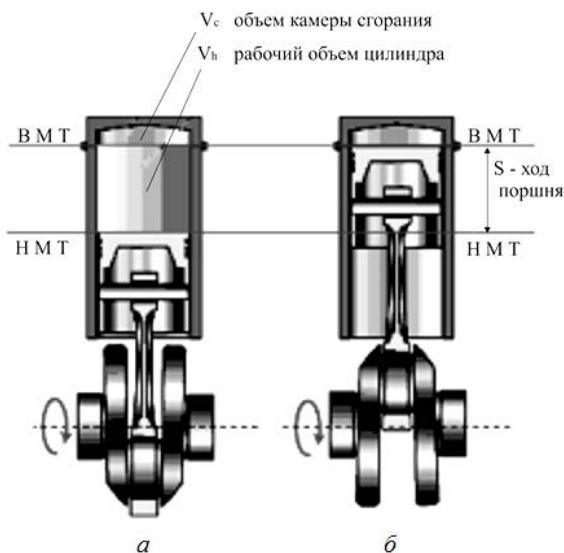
Ход поршня и объемы цилиндра двигателя:
